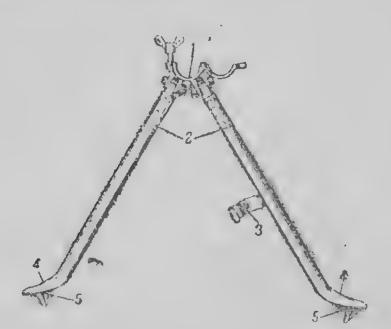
Сошки: 1—хомут; 2—ноги; 3—застежка; 4—башмаки; 5—сошники
